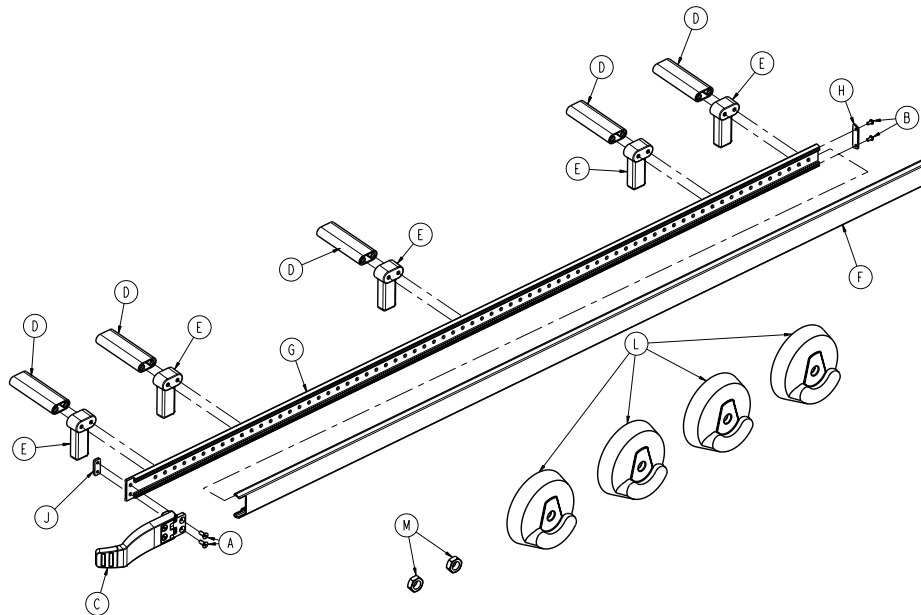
Componentes do kit opcional da guia das rodas - 6390-027-000
